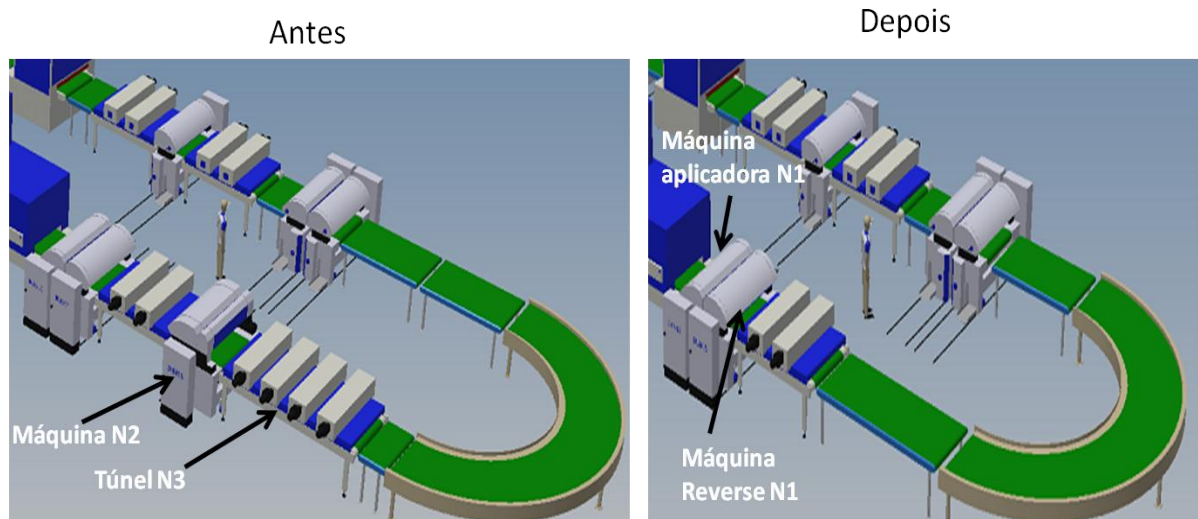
Eliminação máquina verniz N2 (Filler) e Túnel UV N3
